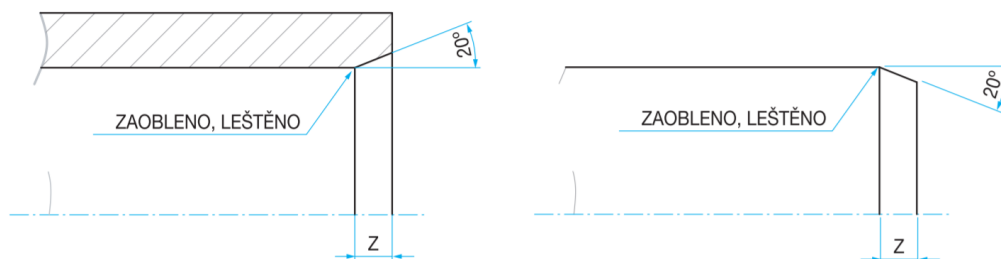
Těsnící prostoru pro trojúhelníkovou drážku [16]
